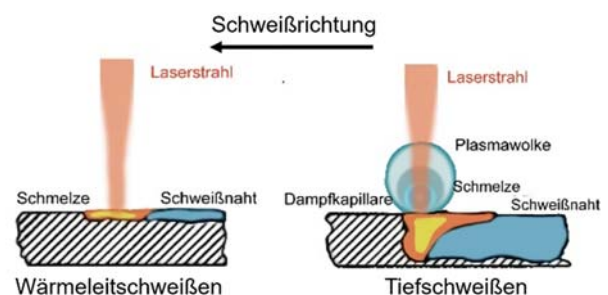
Schema des Laser-Wärmeleitschweißens und des Laser-Tiefschweißens
